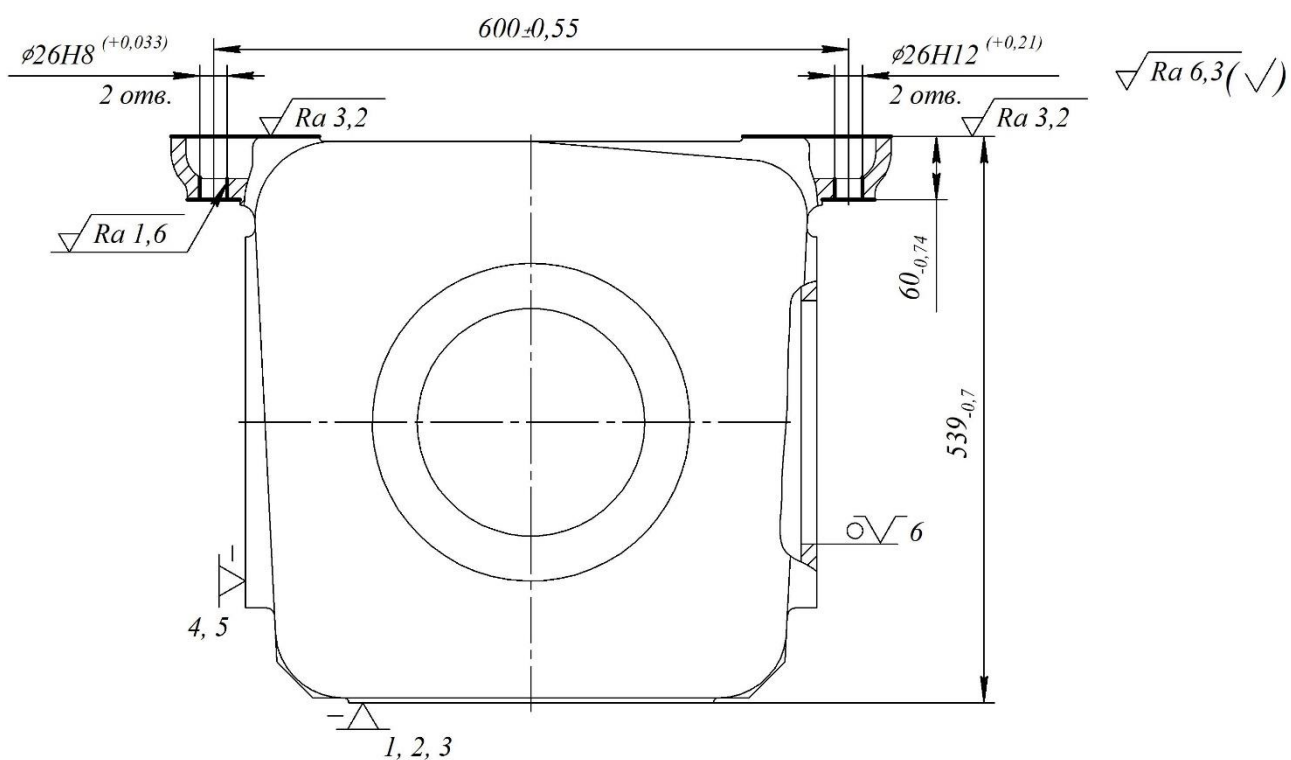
Альтернативна схема базування заготовки на фрезерно-свердильній операції 015
